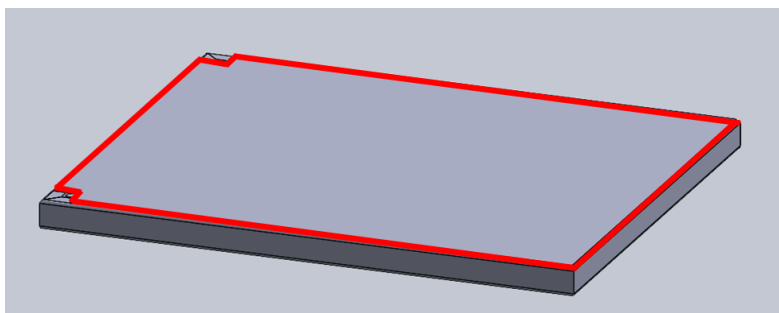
Superficie del cordón de soldadura TIG para la unión CHAPA-CHASIS [fuente propia]
